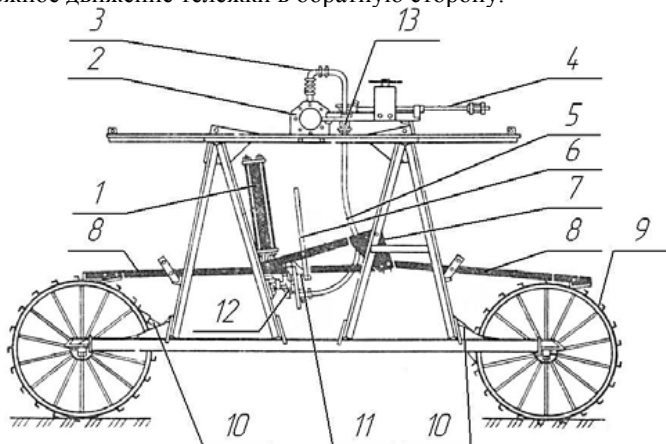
Гидропривод тележки машины «Фрегат»: 1 – гидроцилиндр; 2 – трубопровод водопроводящий; 3 – подводящая труба; 4 – стержень; 5 – напорный рукав; 6 – тяга; 7 – двуплечий рычаг; 8 – толкающие штанги; 9 – колесо тележки; 10 – стопор; 11 – рычаг-переключатель; 12 – клапан-распределитель; 13 – дроссельный клапан.
